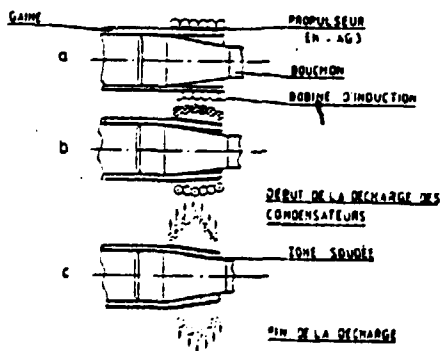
SCHEMA DE PRINCIPE DU SOUDAGE DES BOUCHONS/GAINÉ PAR MAGNETOSOUDEGE
